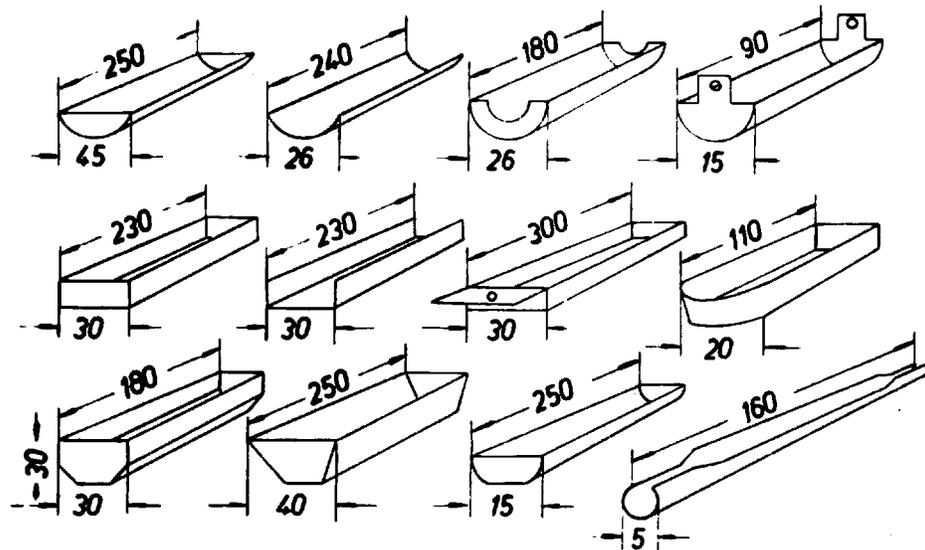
Ausführungsformen von Molybdän-Glühschiffchen.
